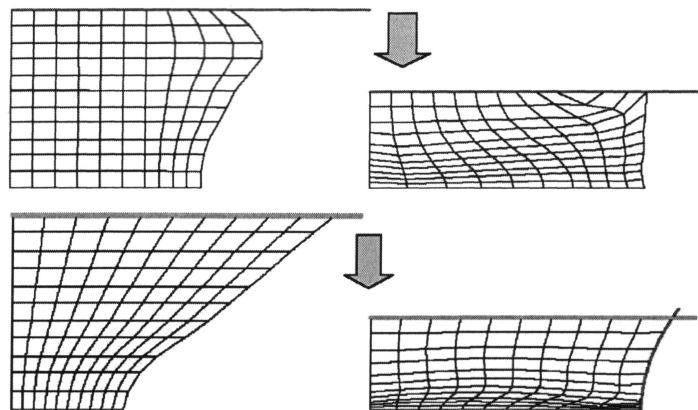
Схема осадки заготовок с различной формой боковой поверхности
